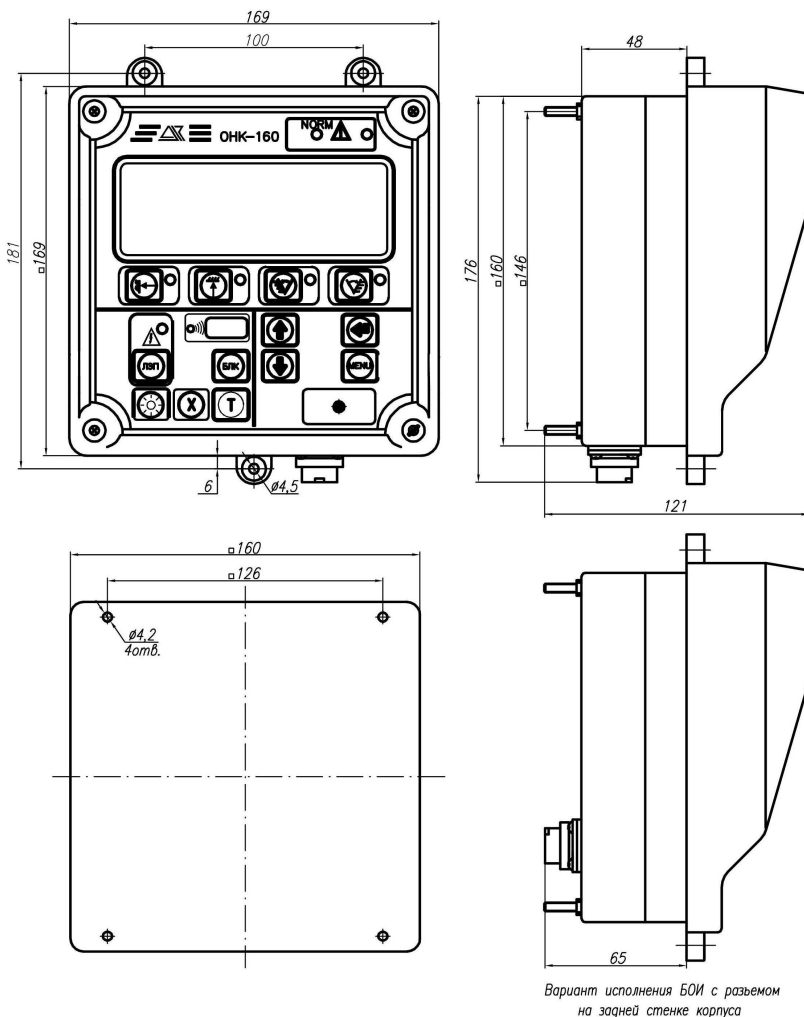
Габаритные и присоединительные размеры БОИ
